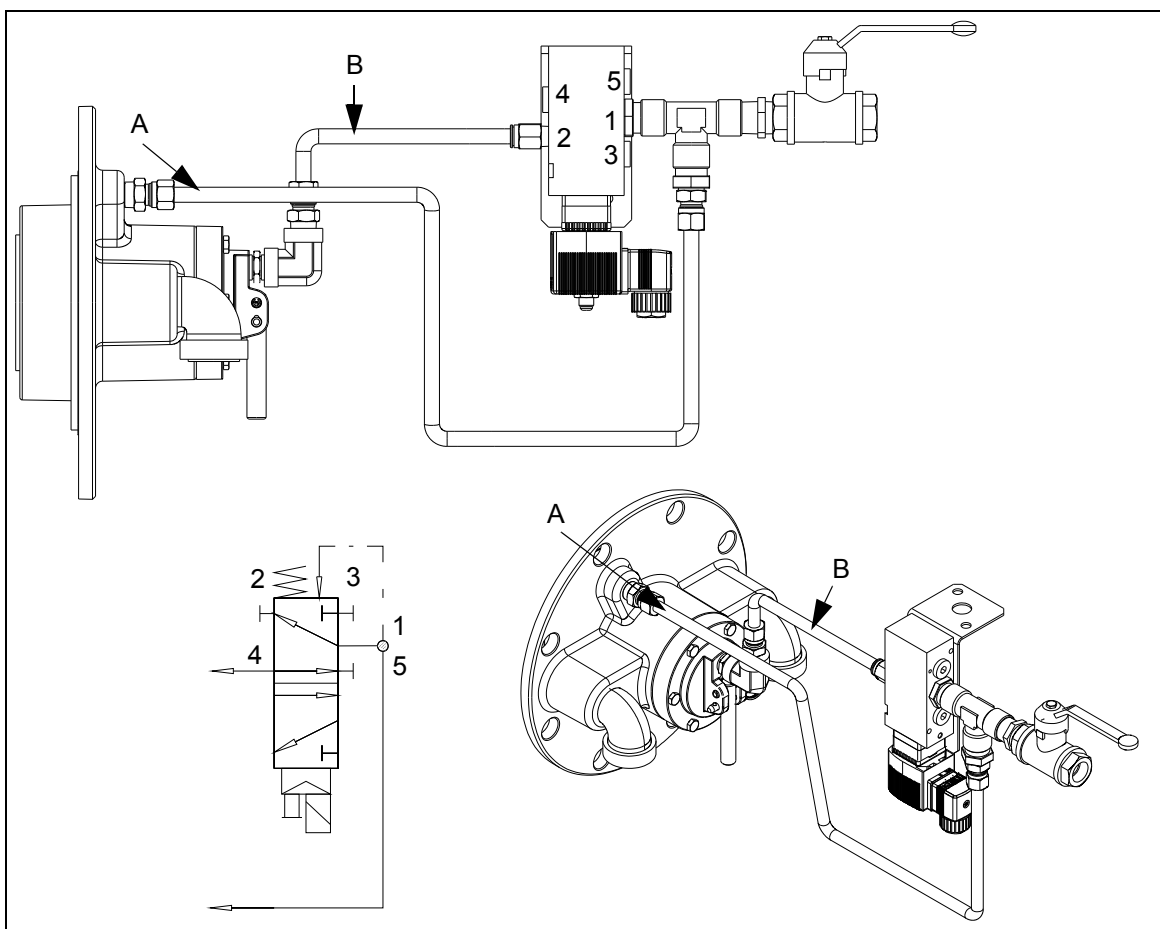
Пневматическое соединение 5/2-ходового электромагнитного клапана - изометрический вид
